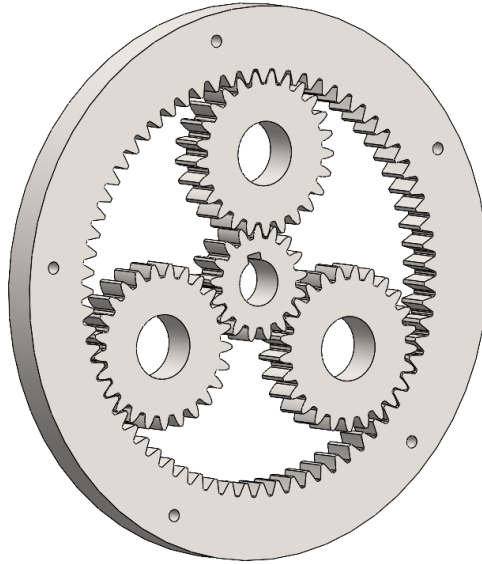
Ensamblaje CAD 3D preliminar de los engranes de la caja de transmisión.
